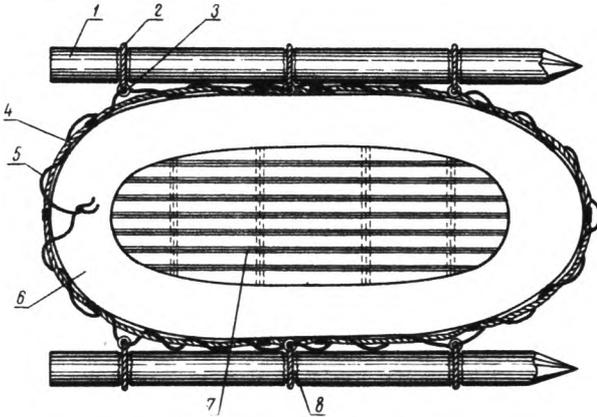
Схематический чертеж монтажа баланси́ров и резиновой лодки: 1 — бревно-баланси́р; 2 — веревка для крепления колец-шарниров; 3 — кольца-шарниры; 4 — спасательный леер лодки; 5 — напрановая веревка для крепления бревен-баланси́ров к лодке; 6 — резиновая лодка; 7 — поёл из реек; 8 — кольцевые фиксирующие затесы.
